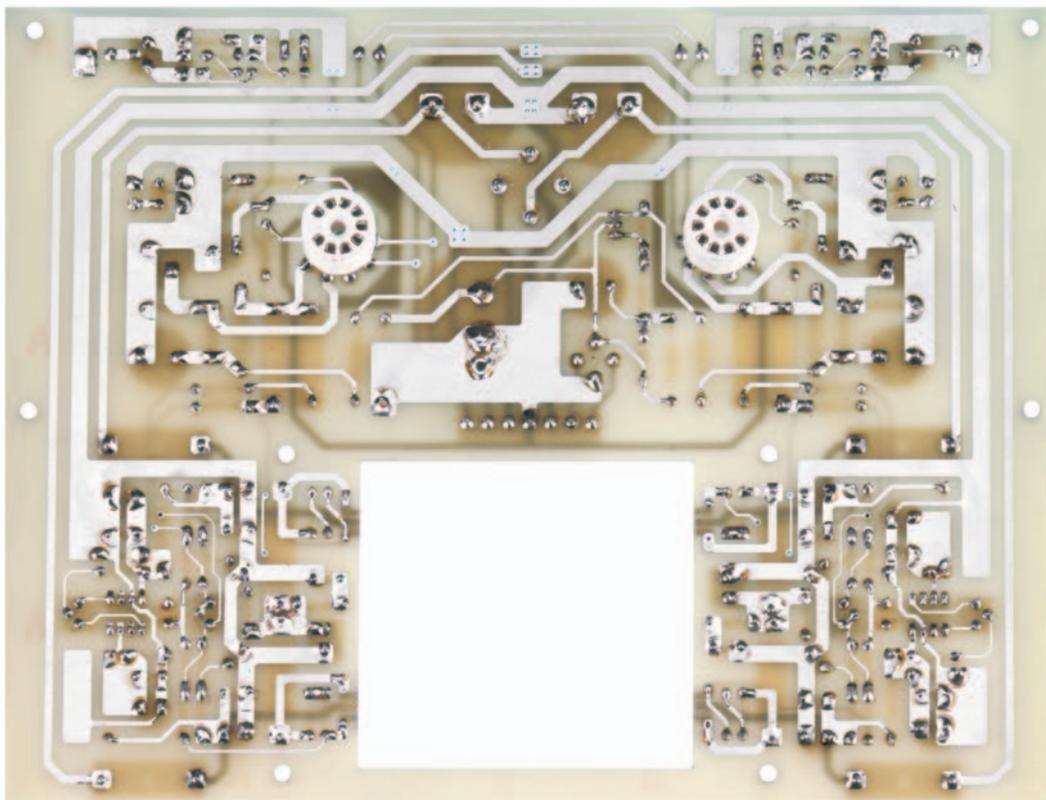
Photo d'un des prototypes de la platine de l'amplificateur, vue face soudures où sont montés les deux supports des doubles triodes ECC82. Le grand évidement carré sert à accéder aux quatre MOSFET, déjà fixés sur le dissipateur extérieur à ailettes, pour la soudure de leurs pattes sur les pistes du circuit imprimé.
